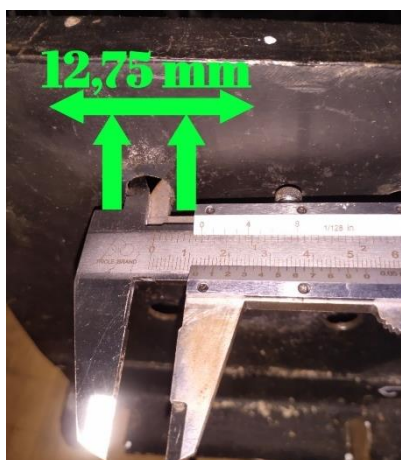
36 Panjang jarak lubang baut 12 wadah pengaduk
